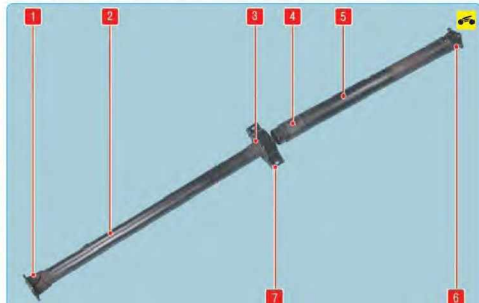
Карданная передача: 1 – карданный шарнир переднего вала; 2 – передний вал карданной передачи; 3 – промежуточная опора карданного вала; 4 – шарнир равных угловых скоростей; 5 – задний вал карданной передачи; 6 – карданный шарнир заднего вала; 7 – кронштейн промежуточной опоры карданного вала
